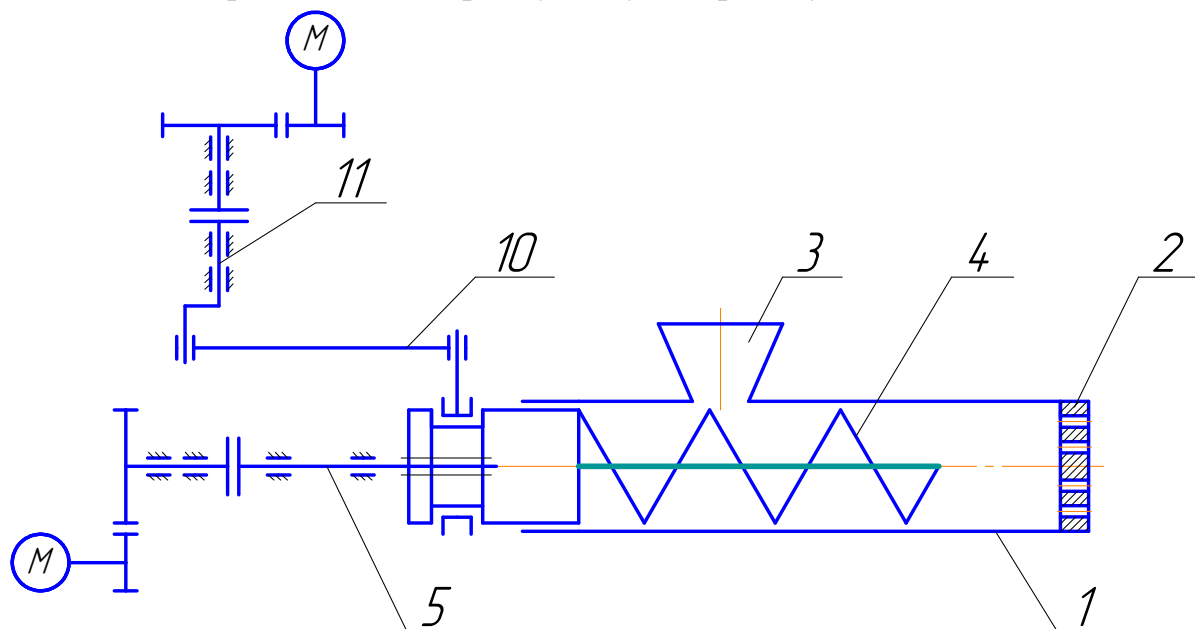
Пресс-экструдер с ползуном кривошипно-ползунного механизма в виде шнека
